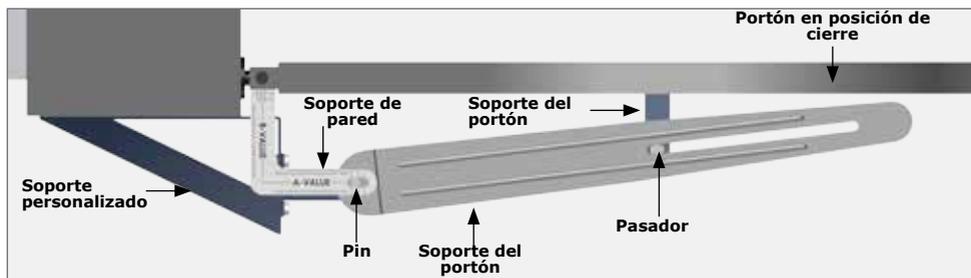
PORTÓN CERRADO (PLANTILLA DE METAL MONTADA)
